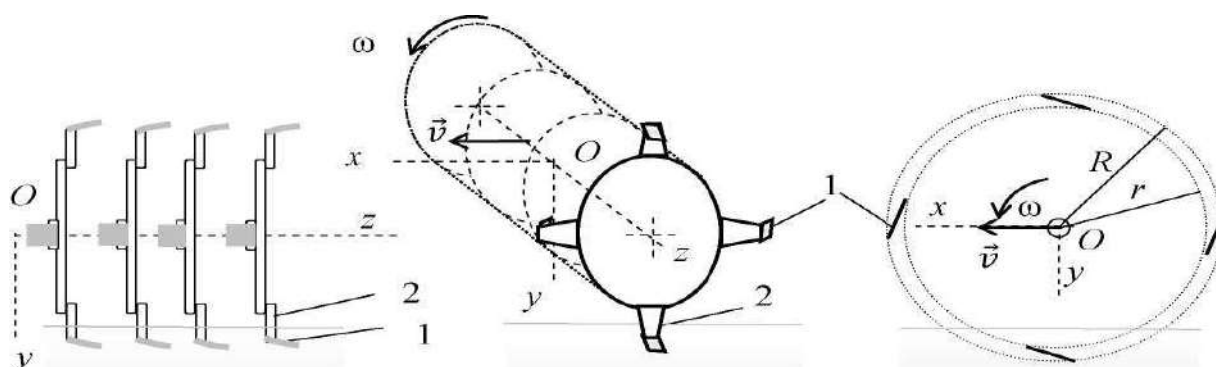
Барабан фрези з ножами 1 і боковинами з ріжучими крайками 2
